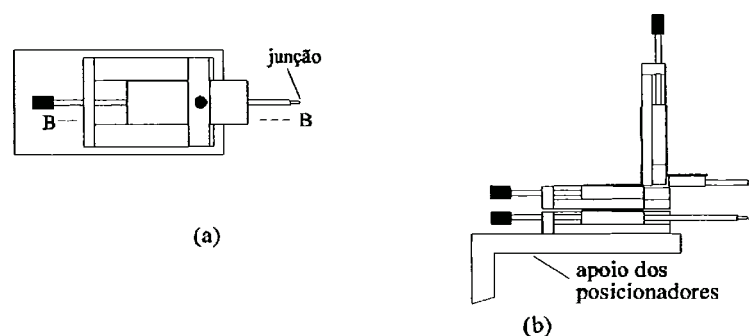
(a) vista superior dos posicionadores, (b) corte BB.
